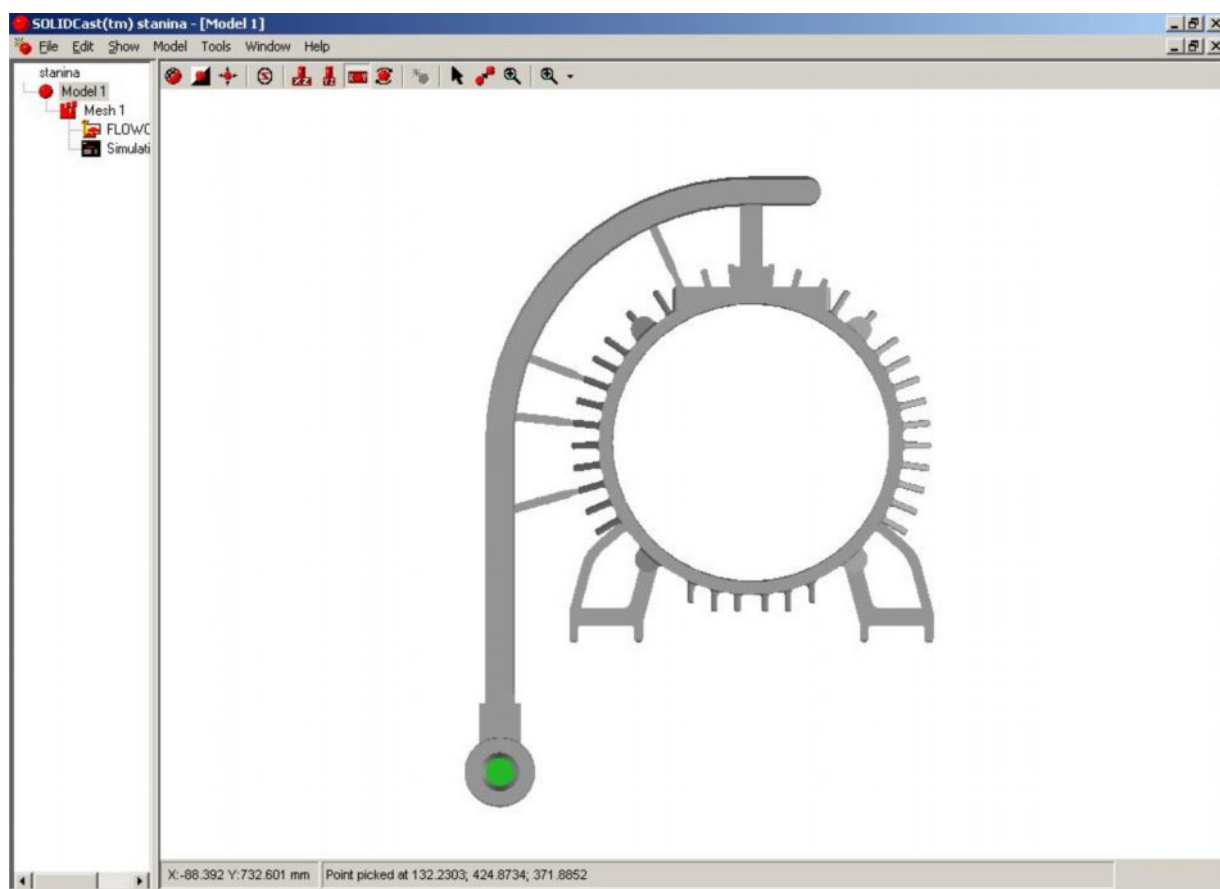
Общий вид отливки “Корпус электродвигателя”
